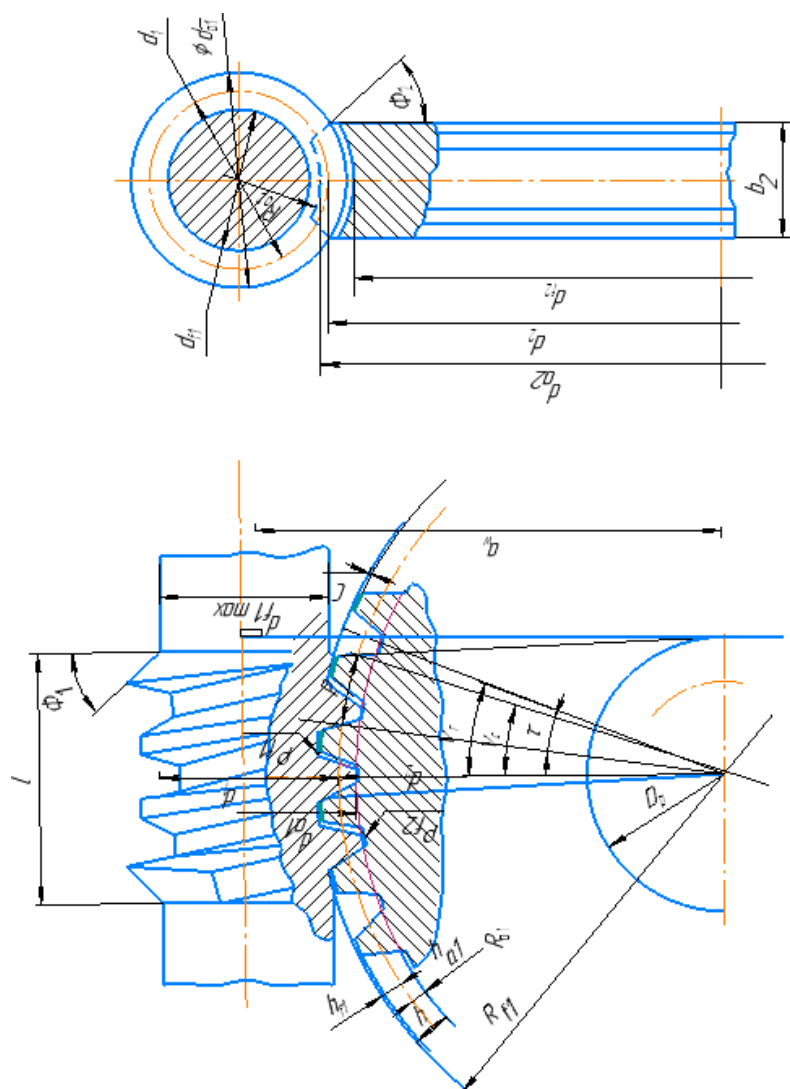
Геометрия червячной глобоидной передачи с верхним расположением червяка
